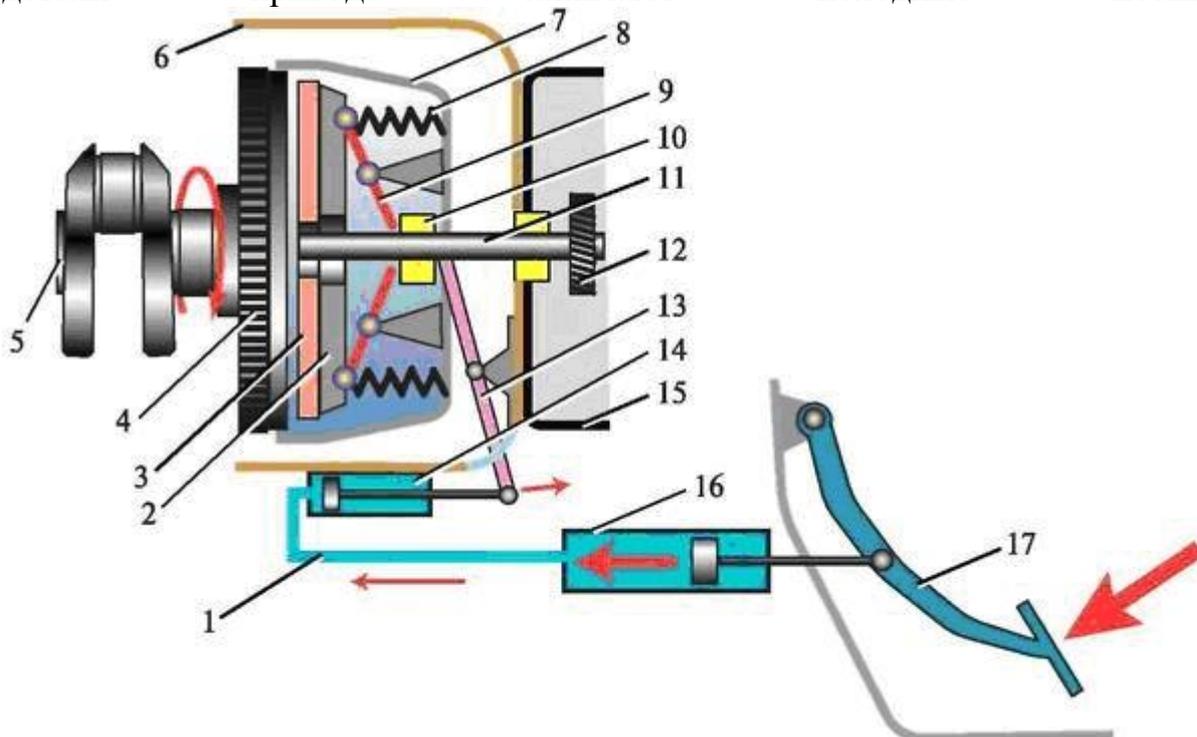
Схема гидравлического привода выключения сцепления и механизма сцепления: 1 - трубопровод; 2 - нажимной диск; 3 - ведомый диск; 4 - маховик; 5 - коленчатый вал; 6 - картер сцепления; 7 - кожух сцепления; 8 - нажимные пружины; 9 - отжимные рычаги; 10 - выжимной подшипник; 11 - первичный вал коробки передач; 12 - шестерня первичного вала; 13 - вилка выключения сцепления; 14 - рабочий цилиндр; 15 - картер коробки передач; 16 - главный цилиндр; 17 - педаль сцепления
